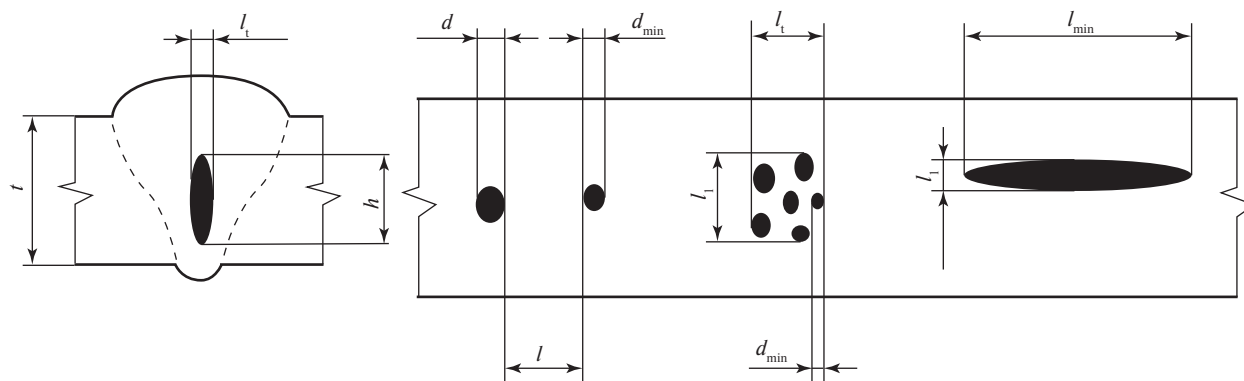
Схематическое изображение сварного шва и определение размеров дефектов
